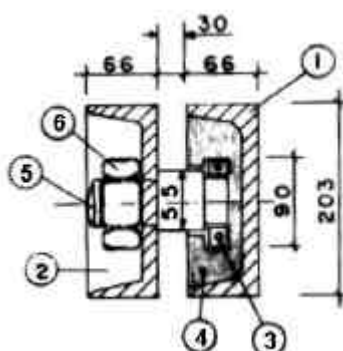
Detalhe A com vista do perfil da viga e mancal da viga
